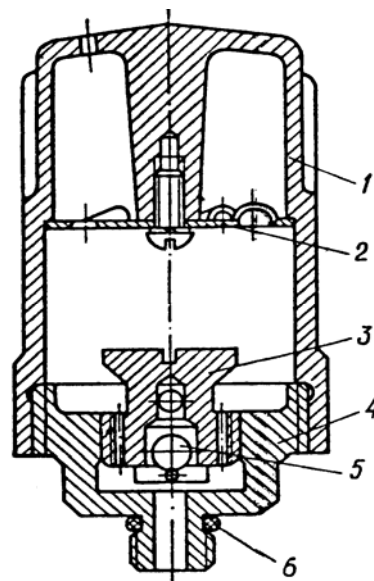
Оливоуловлювач вимикача ВММ-10: 1 - кришка; 2 - оливоуловлювач; 3 - корпус клапана; 4 - підставка; 5 - кулька; 6 - ущільнення
